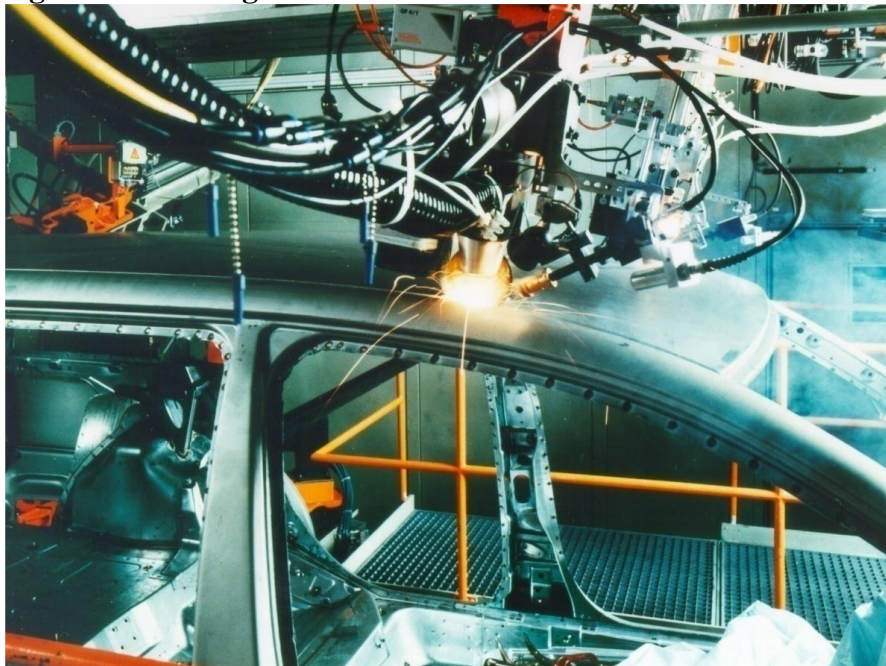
Soldagem GMAW robotizada de carroceria automotiva.
